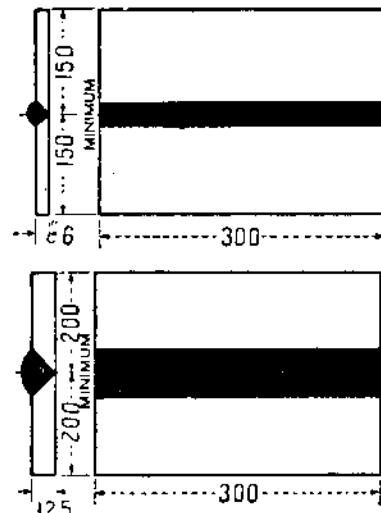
Сварка встык односторонним V-образным швом.
